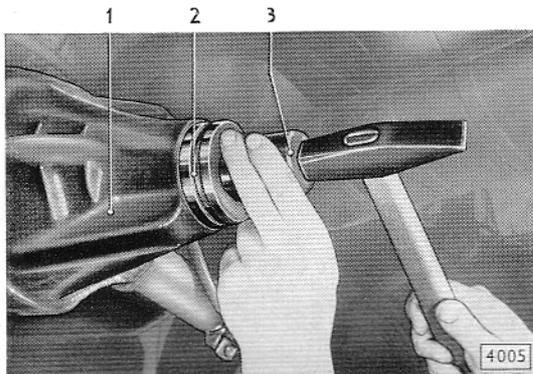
Dichtring für Antriebskegelrad einschlagen
